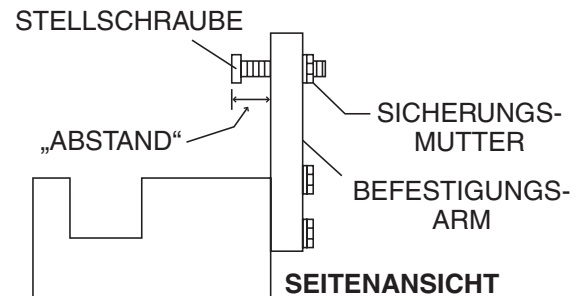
Einstellwerkzeug des Glättarms (Seitenansicht)
